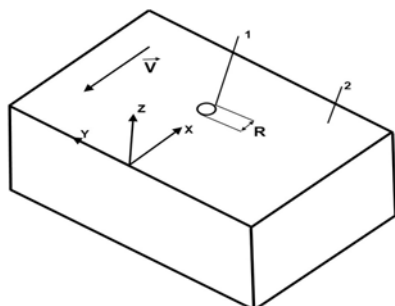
Схема расположения лазерного пучка в зоне обработки
